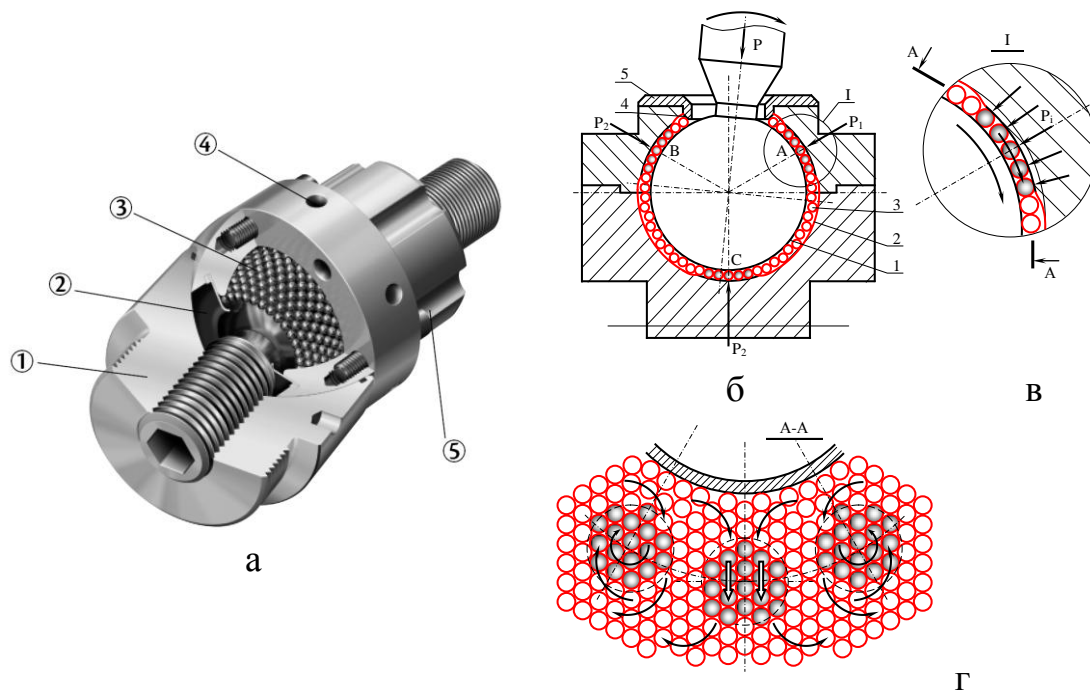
Сферичний шарнір з кульовими тілами кочення без сепараторного типу: а – конструктивна схема; б – перетин шарніра; в – розташування несучих тіл кочення між сферичними поверхнями; г – циркуляція тіл кочення в зазорі між сферою і охоплюючою поверхнею
